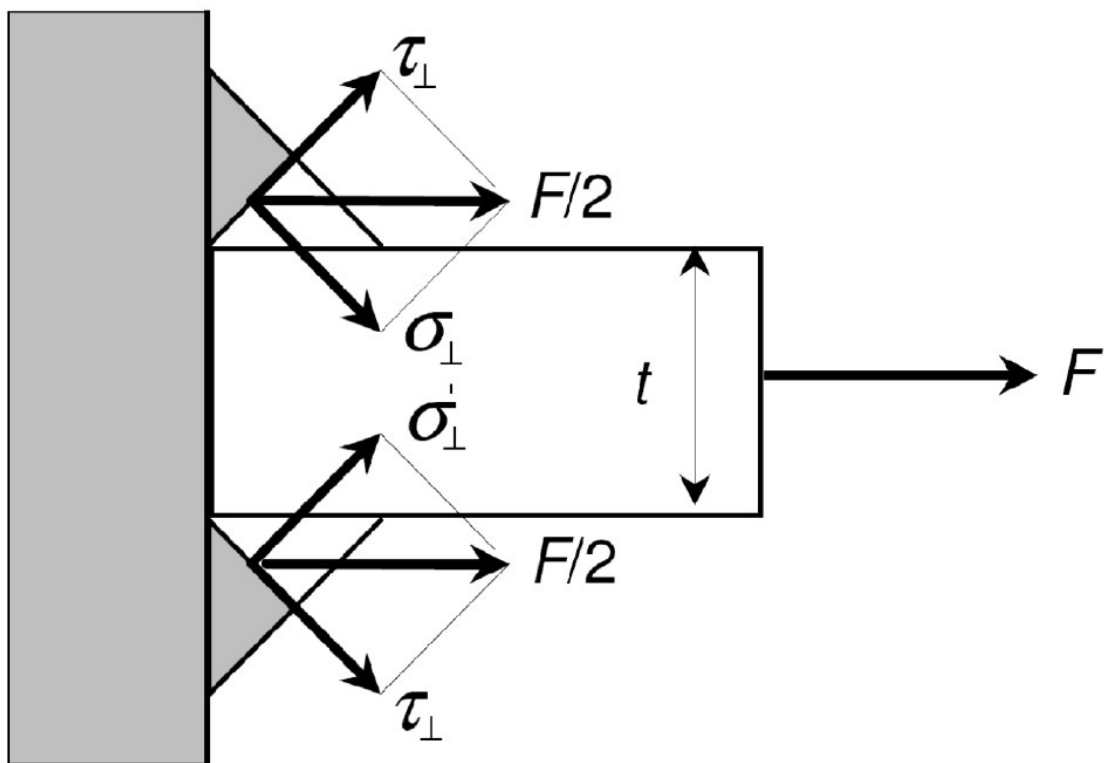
Doppelkehlnahtanschluss mit Beanspruchung rechtwinkelig zur Schweißnaht gemäß DIN EN 1999-1-1:2014-03 Abschnitt 8 Bild 8.19
